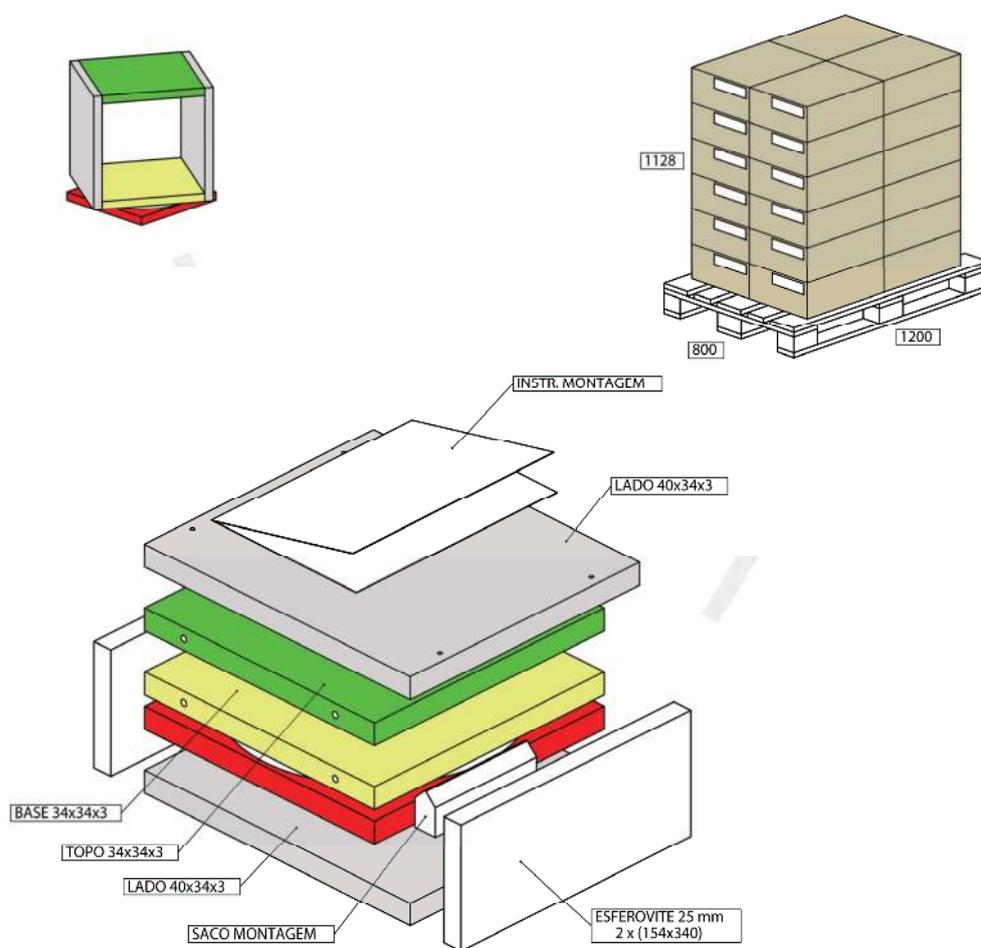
Instrução de embalagem estante shell ⁵⁶
